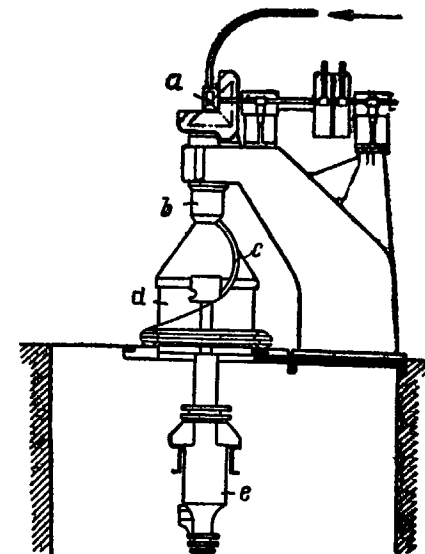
Моталка с неподвижным барабаном старой конструкции
